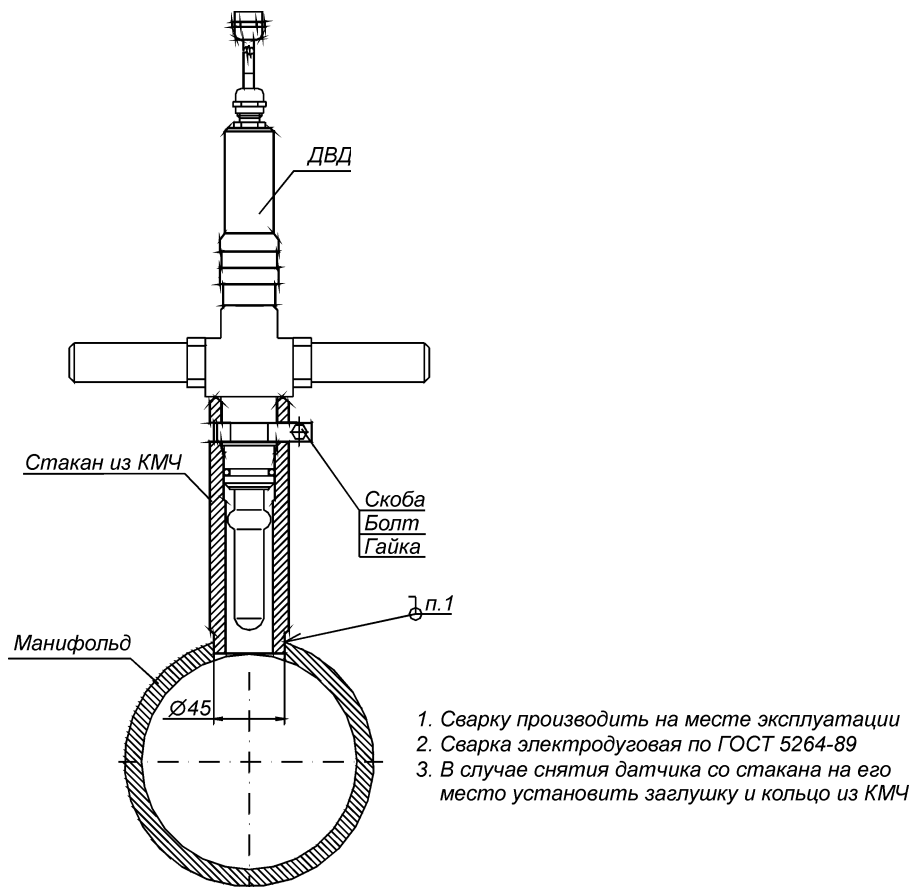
ДВД-320-06. Монтажный чертеж
